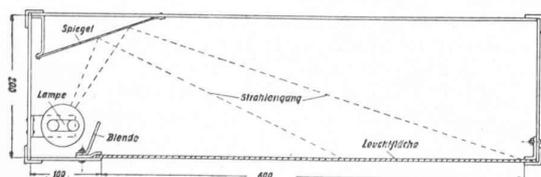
Coupe transversale d'un transparent à une face éclairante.
